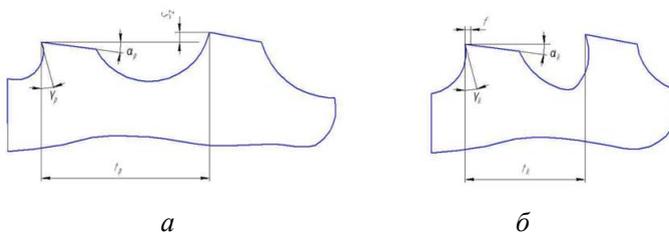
Конструкция режущих (а) и калибрующих (б) зубьев рабочей части протяжки
